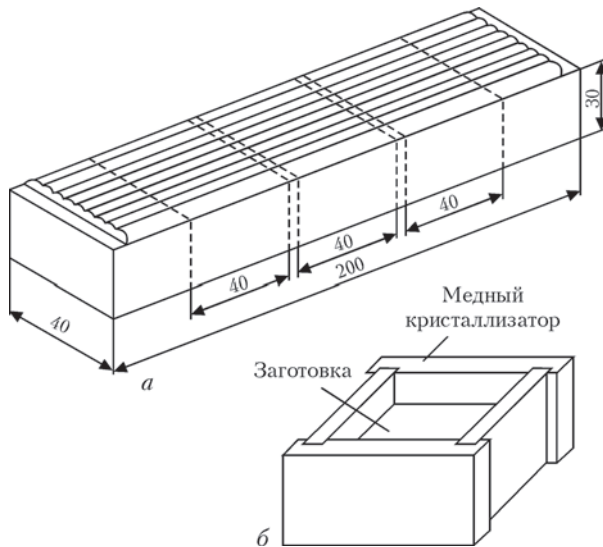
Схема изготовления многослойных наплавленных образцов для исследования термической стойкости: а — при автоматической наплавке под флюсом; б — при полуавтоматической наплавке самозащитными порошковыми проволоками заготовки из стали 40Х производилась электродуговая наплавка рабочего слоя порошковой проволокой ПП-Нп-25Х5ФМС по следующим вариантам: наплавка без подслоя и наплавка рабочего слоя с подслоем, наплавленным проволокой Св-08А. Учитывая, что на термическую усталость значительное влияние оказывают концентраторы напряжений, резкие переходы формы, структурная неоднородность и т.д. [1, 2], было высказано предположение, что глубина и форма проплавления также влияют на термическую стойкость металла. Исходя из этого, наплавка опытных образцов проводилась по двум технологиям:
